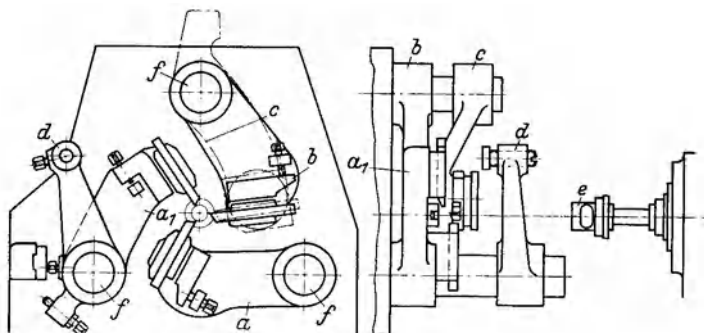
Schraubensautomat mit schwingenden Werkzeugträgern (Index).
